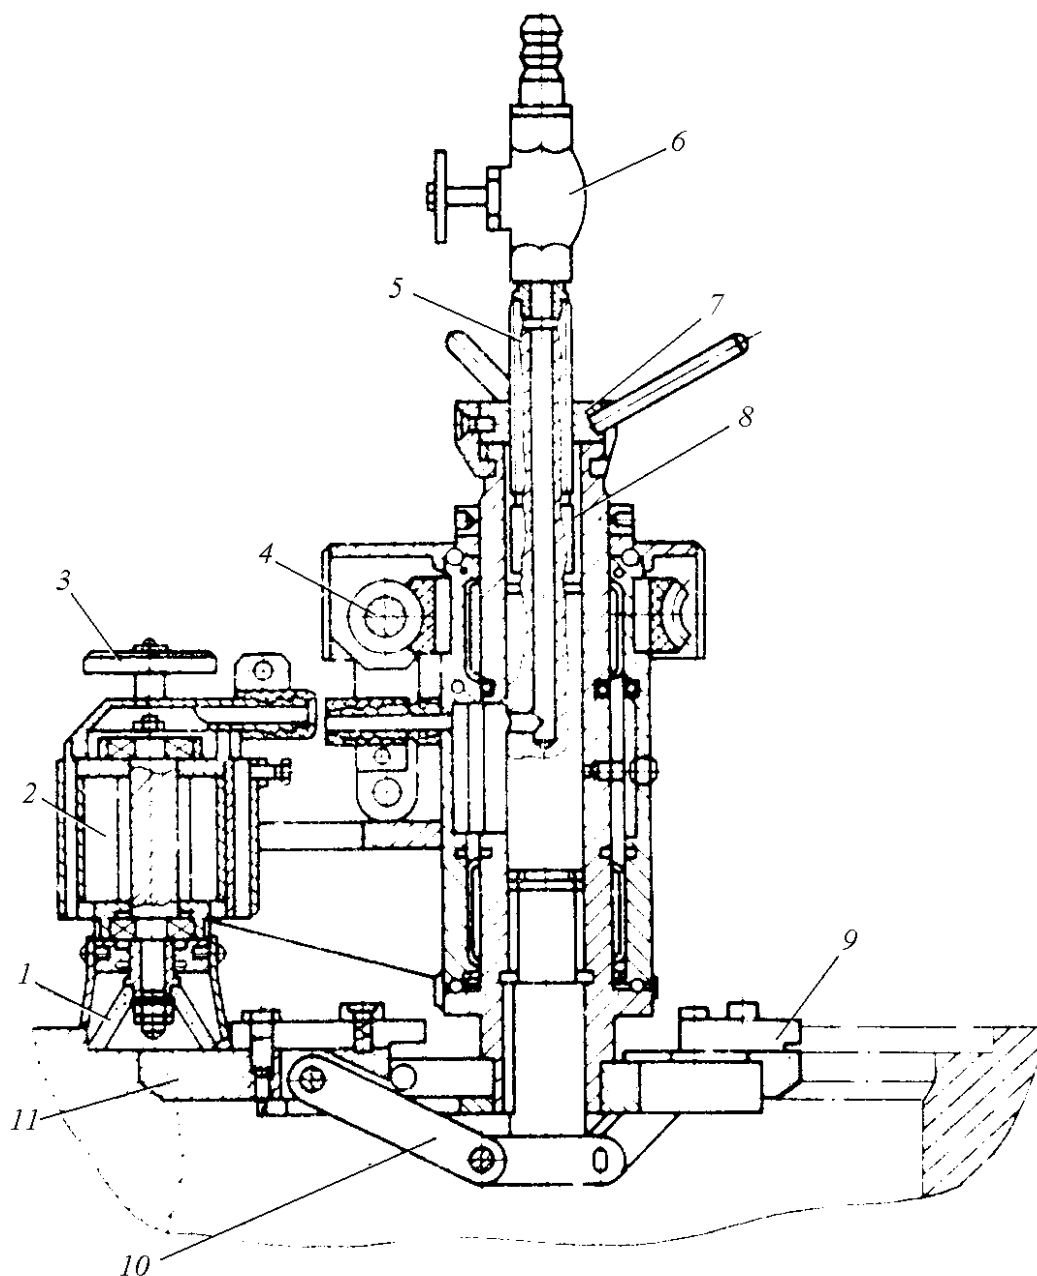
Приспособление для шлифовки уплотнительных поверхностей корпусов задвижек с D_y 100—300 мм под гребенчатые прокладки.
